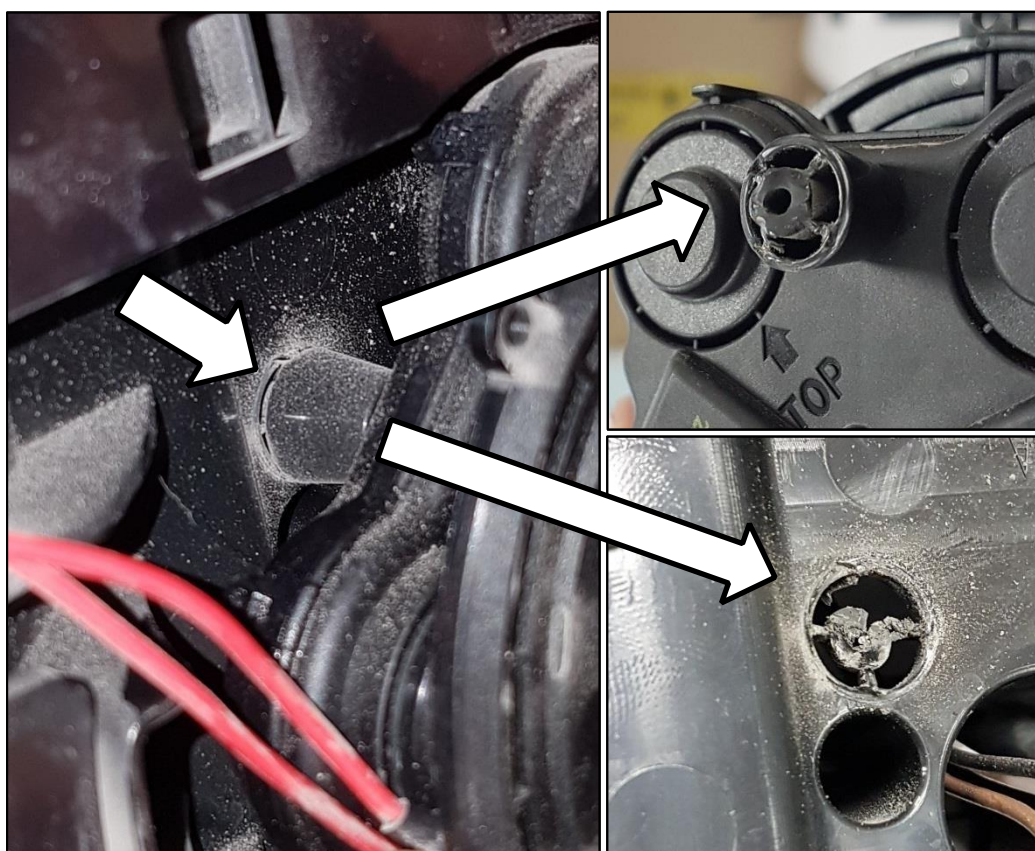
Разрушение крепёжной бобышки моторедуктора
